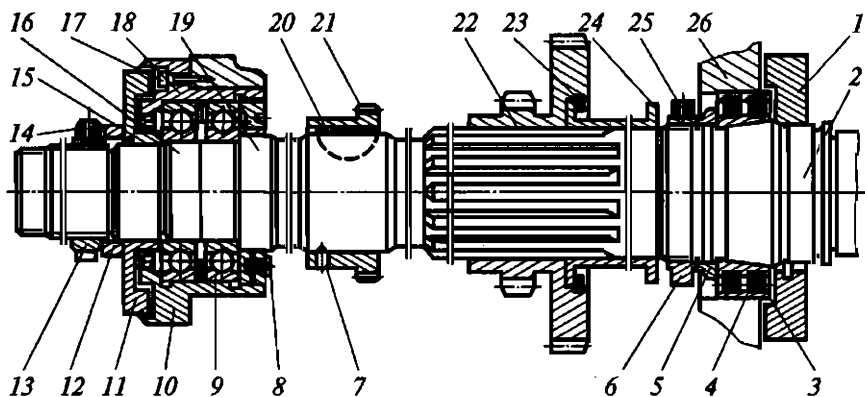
Шпиндельный узел токарно-винторезного станка:
